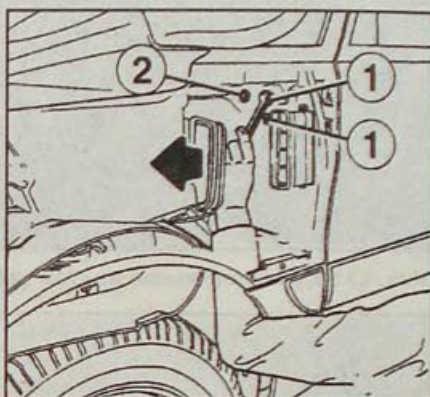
Расположение гаек крепления балки в арке переднего колеса:
